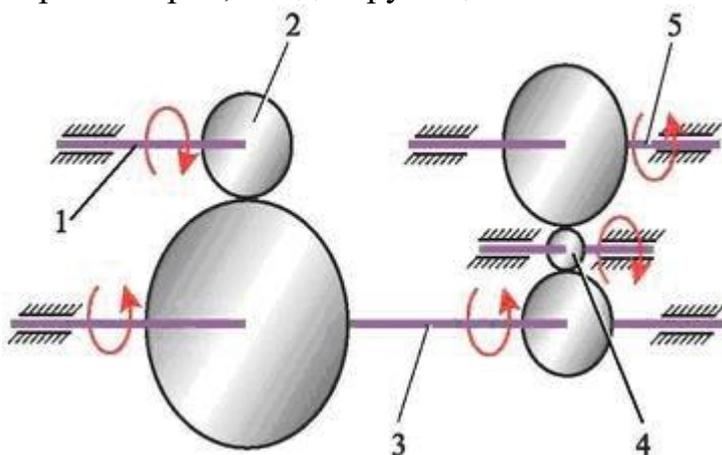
Схема передачи крутящего момента при включении задней передачи: 1 - первичный вал; 2 - шестерня первичного вала; 3 - промежуточный вал; 4 - шестерня передачи заднего хода; 5 - вторичный вал. Поскольку в коробке передач реального автомобиля имеется большой набор шестерен, то, вводя в зацепление различные их пары (включая различные передачи), мы изменяем и общее передаточное отношение.
